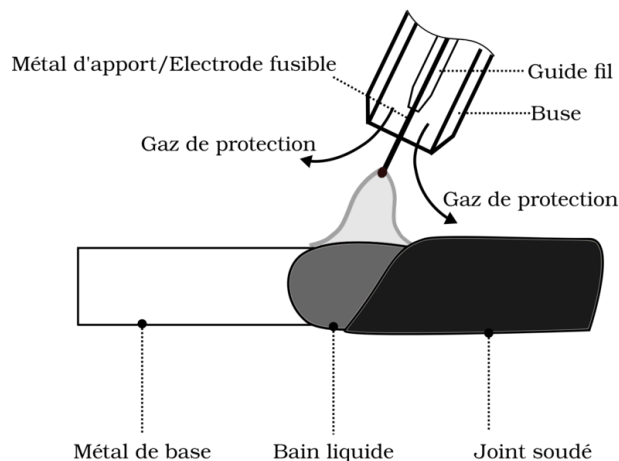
Coupe longitudinale d'une opération de soudage MAG.
